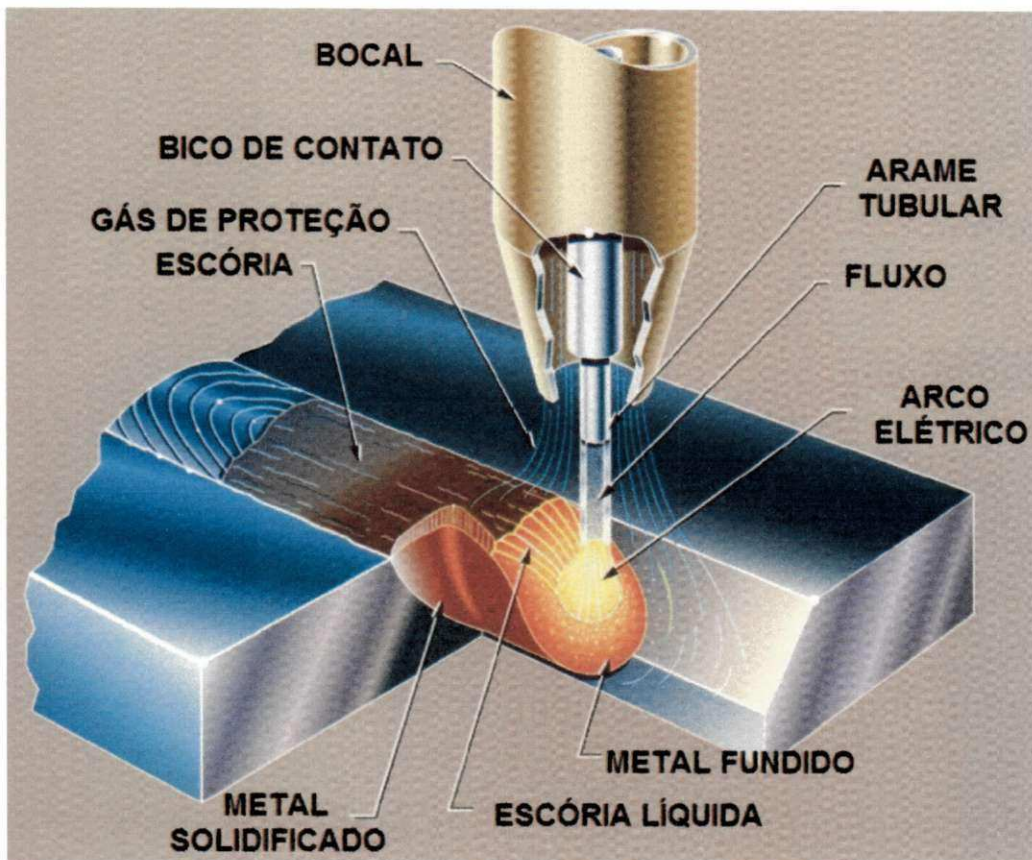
Esquema de soldagem com arame tubular pelo processo FCAW-G adaptado de Welding Handbook (1991).
